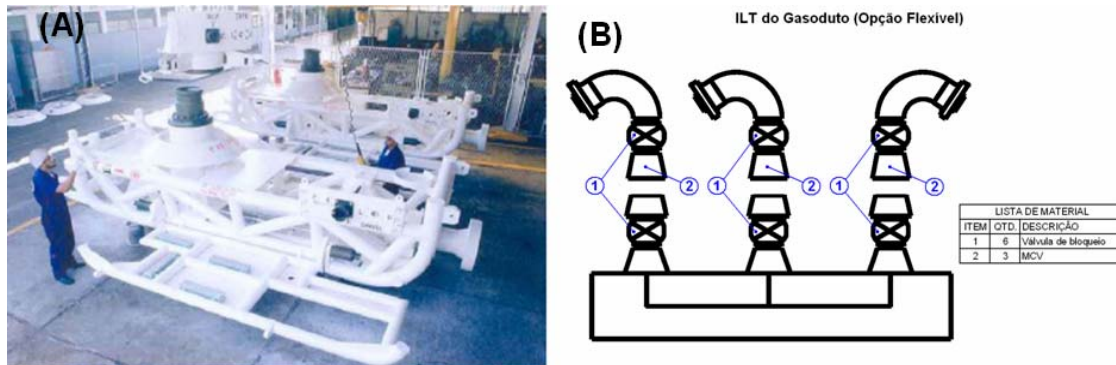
Foto e ilustração de elementos de interligação (a) PLET (b) ILT
